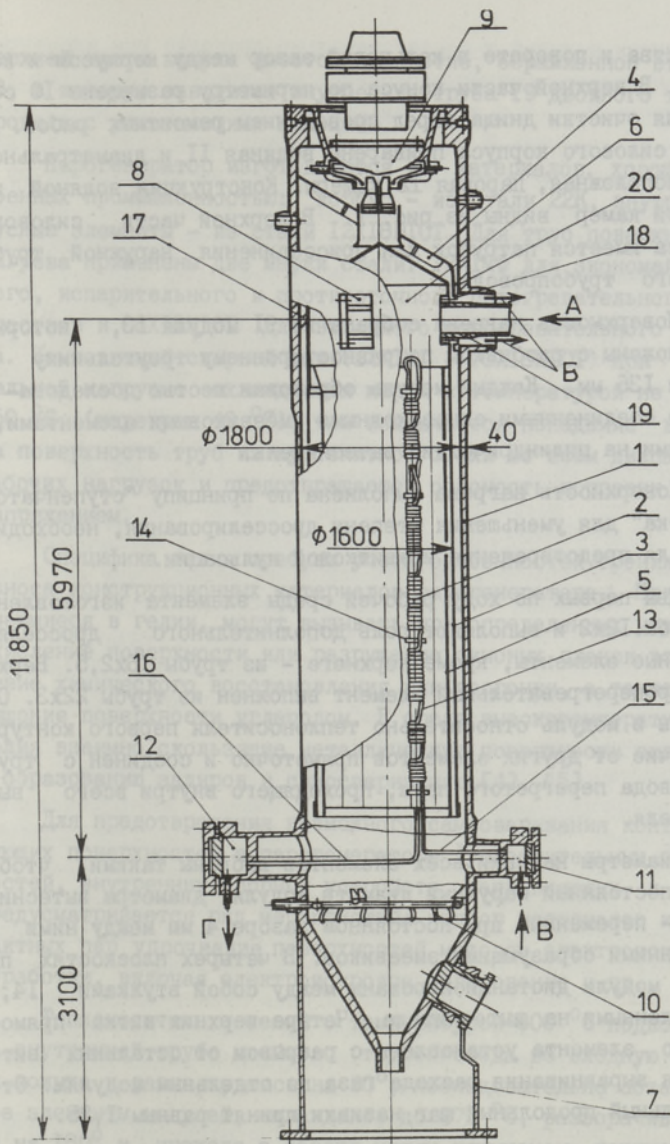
Парогенератор установки с ВГР-50: 1 - силовой корпус, 2 - поверхность нагрева, 3 - кожух цилиндрический, 4 - перегородка плоская, 5 - вытеснитель шестигранный, 6 - выходная камера, 7 - нижняя опора, 8 - седловая опора, 9 - газодувка, 10 - обдувочные сопла, 11 - водяная камера, 12 - паровая камера, 13 - модуль, 14 - дистанционирующие втулки, 15 - соединительные трубы питательной воды, 16 - соединительные трубы острого пара, 17 - опоры кожуха, 18 - втулка кожуха, 19 - внутренняя труба двойного трубопровода, 20 - карман. А - вход гелия, Б - выход гелия, В - вход питательной воды, Г - выход перегретого пара.
